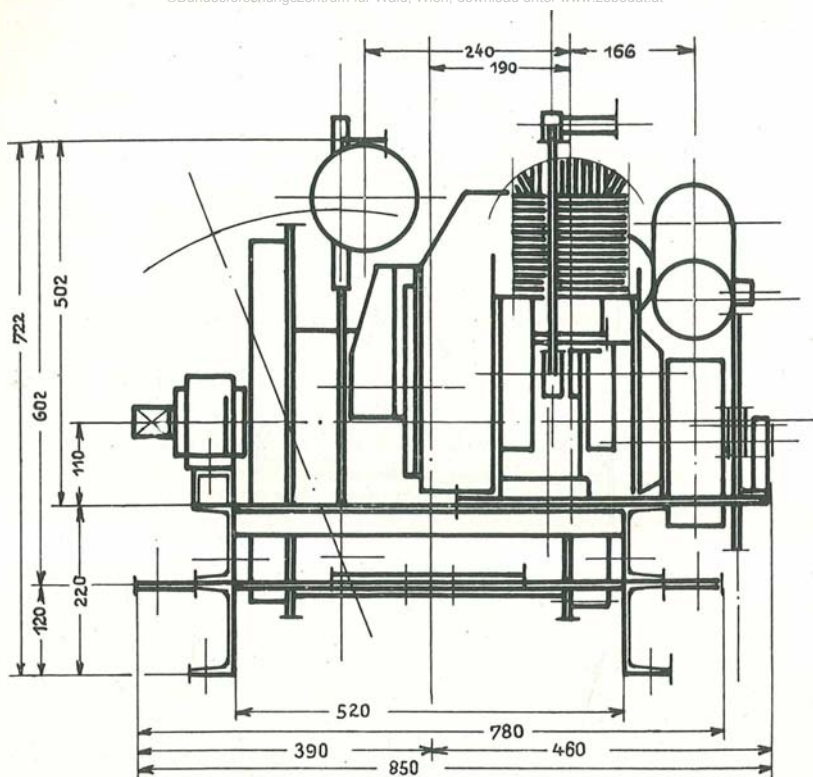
Desgleichen. Rückansicht mit dem Motor.
